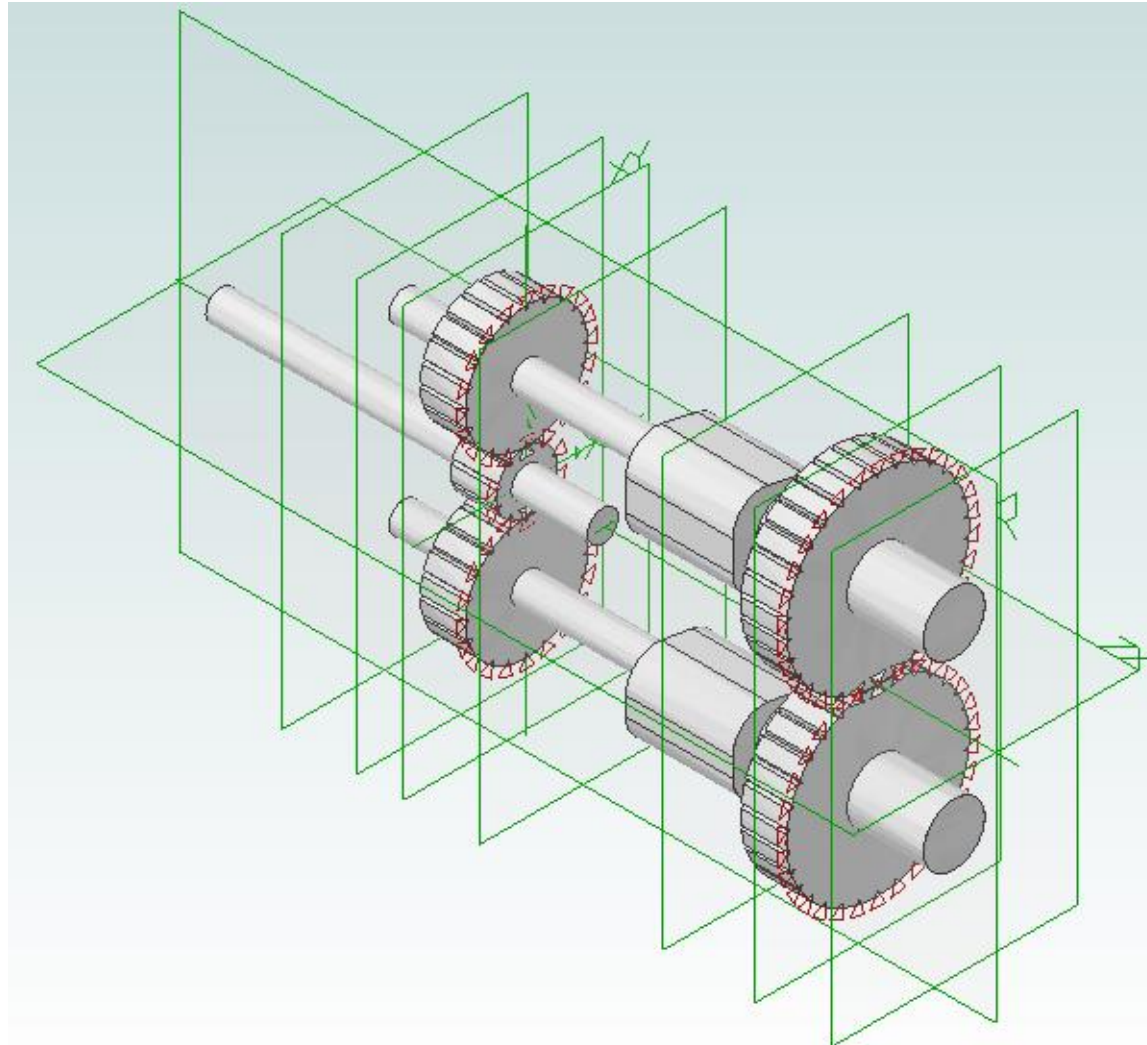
Engrenagens que transferem movimento para o veio de saída/Gears transferring power to output shaft.
